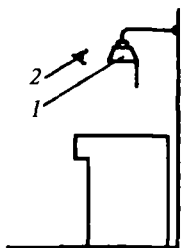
Схема контроля деталей «на просвет»: 1 — ОП; 2 — положение глаз работающего
